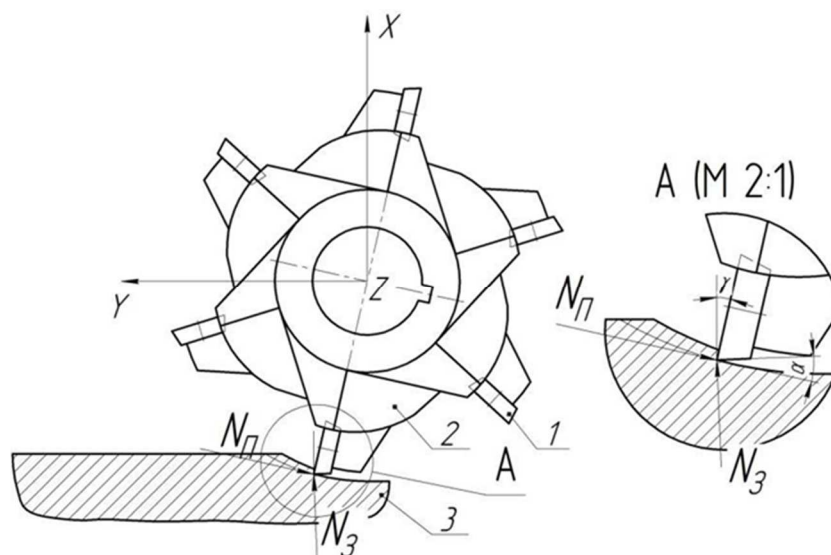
Методика воздействия сил на зуб инструмента в ходе резания: 1 – пластина; 2 – корпус; 3 – заготовка
